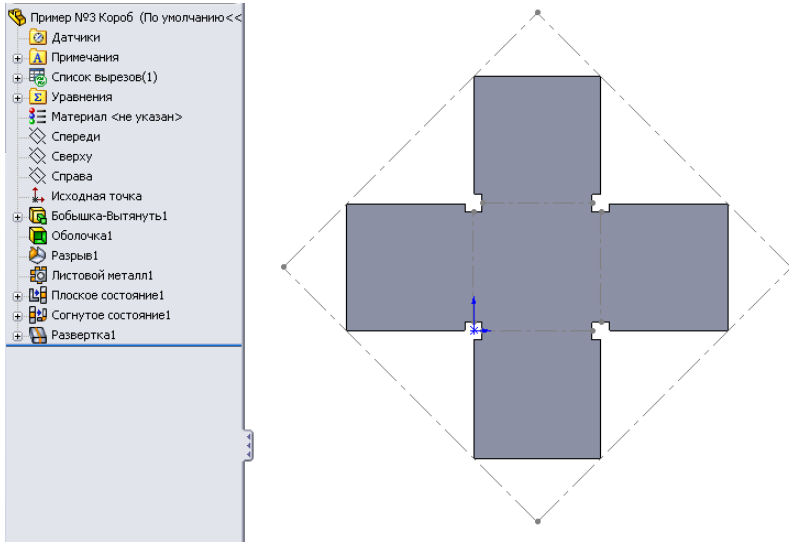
Деталь розгорнута в площині основи короба
